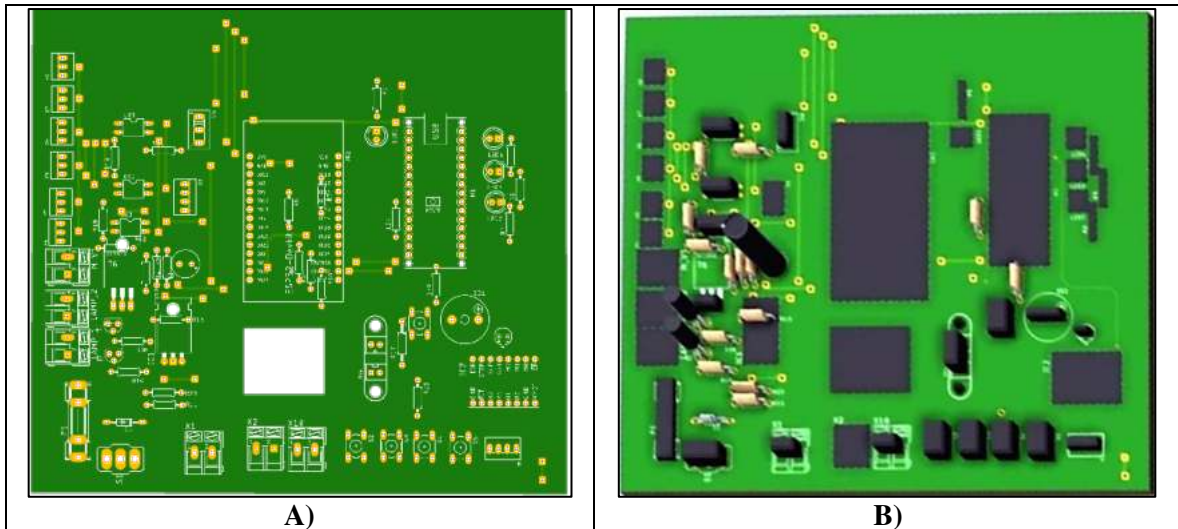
A) Placa diseñada en Eagle Anverso. B) Vista en 3D de la placa
